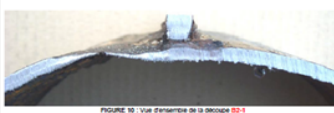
Vue d'ensemble de la découpe B2.1 (zone de perforation et corrosion en surface extérieure du tube).
